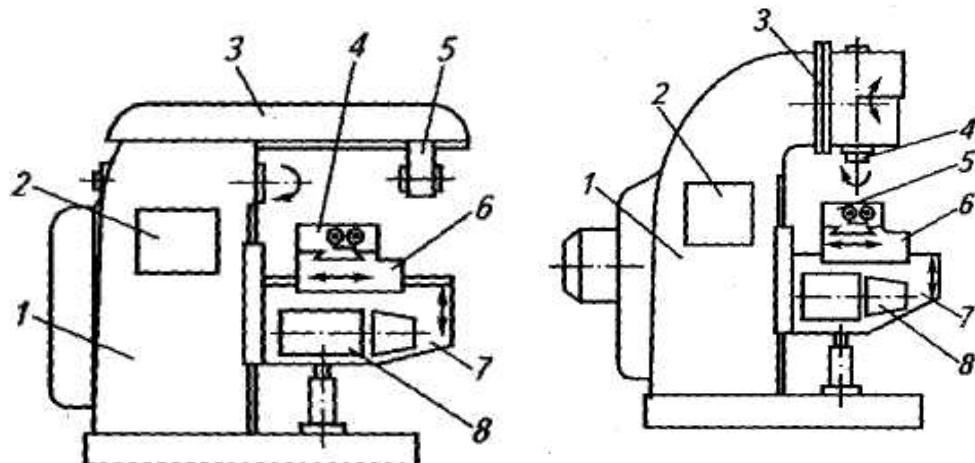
Общий вид горизонтально-фрезерного станка:
